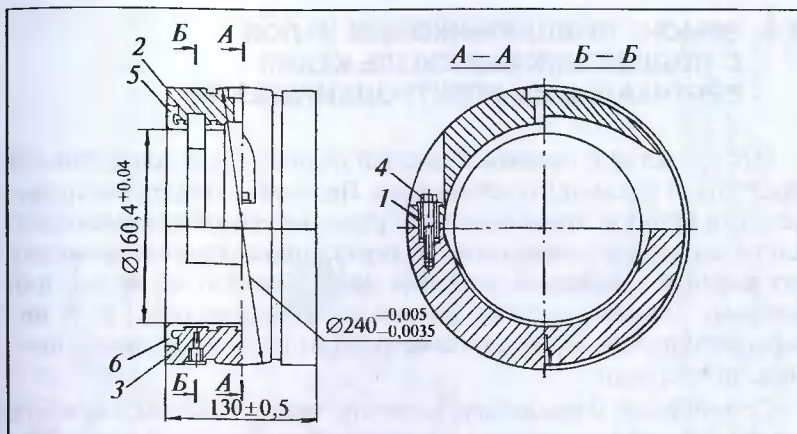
Вкладыш подшипника электродвигателя 4АЗМ-5000/6000УХЛ4:
